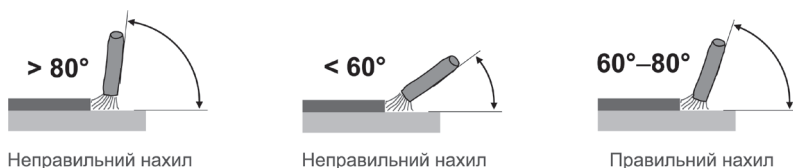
Кут розташування електрода із покриттям до деталі під час ручного дугового зварювання («ММА»).
